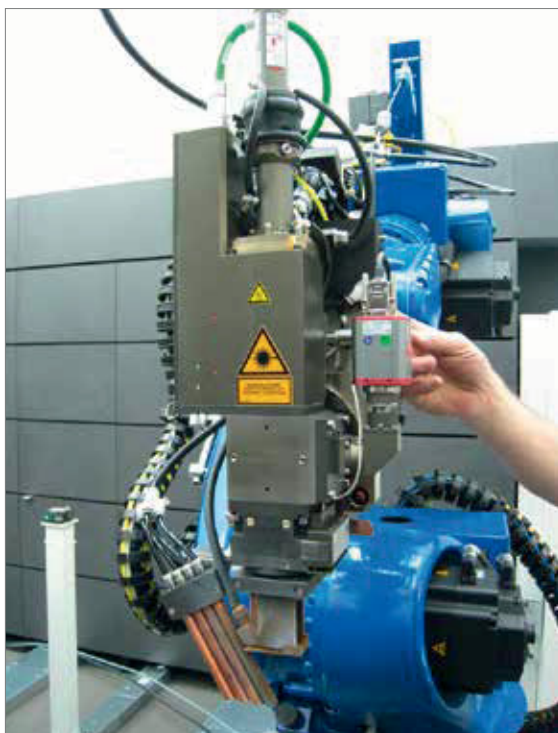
Nd:YAG-Laser zur Metallbearbeitung
